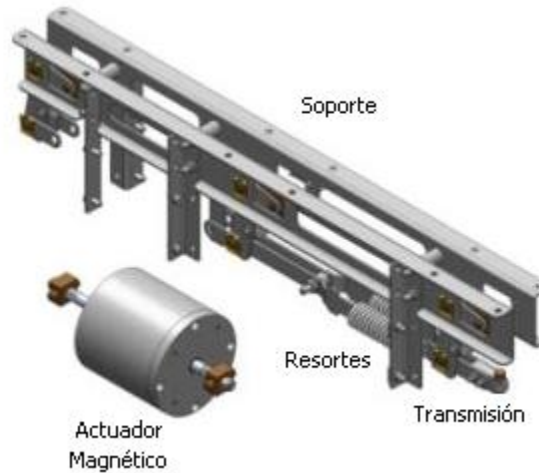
Actuador Magnético con mecanismo de transmisión.
